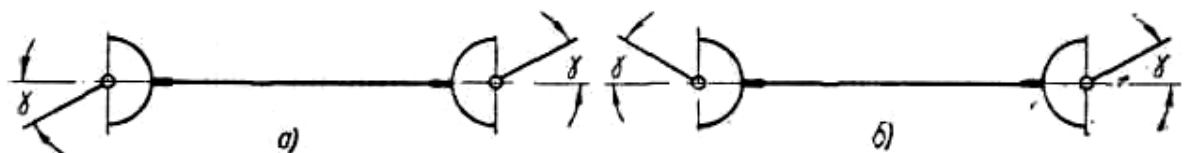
Схеми двохшарнірної передачі з рівномірним обертанням вихідного валу
